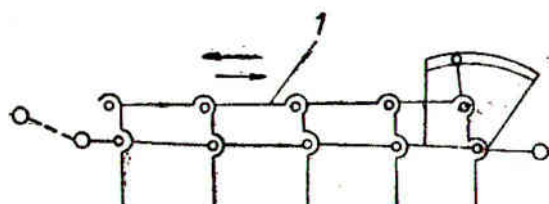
Mecanism de reglare a poziției colților în plan vertical
